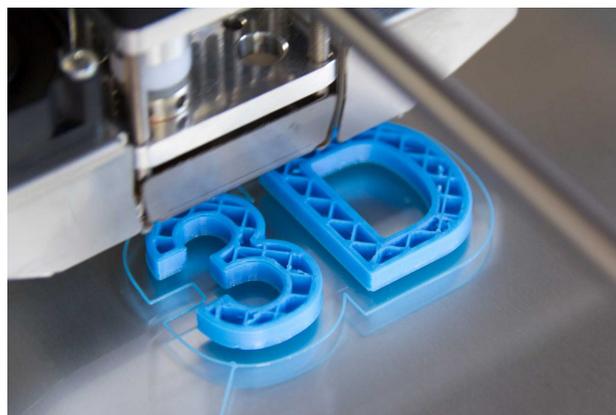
Proceso de impresión 3D. Fuente: intech3d.es
